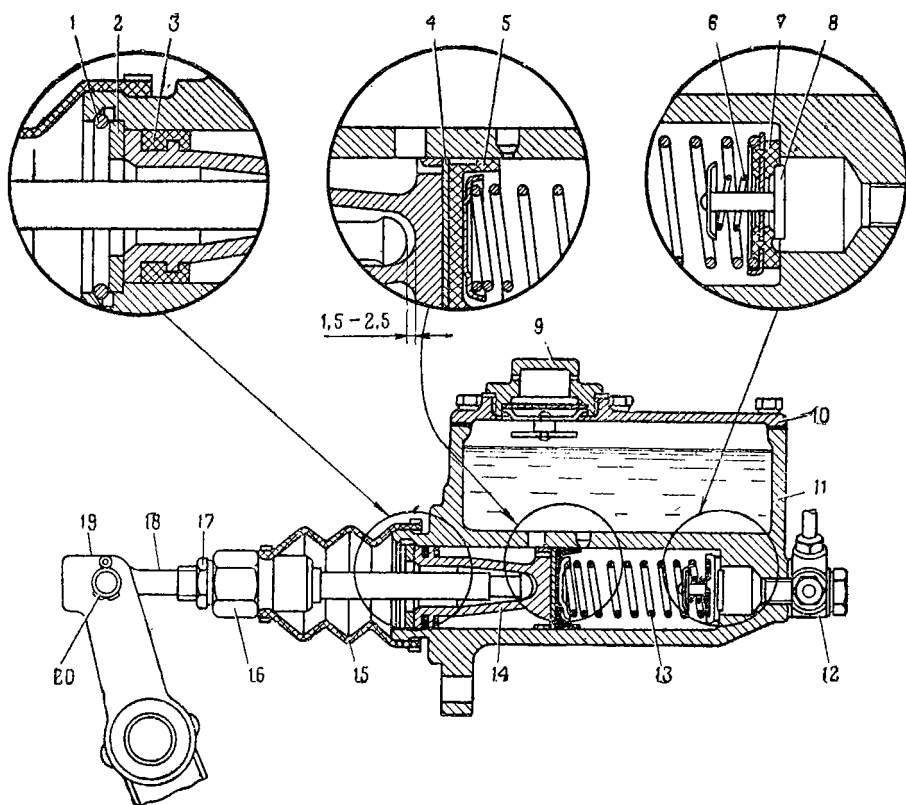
Регулировка зазора между толкателем и поршнем главного цилиндра: 1 — пружинное кольцо; 2 — упорная шайба; 3 — уплотнительное кольцо; 4 — звездообразная плоская пружина; 5 — манжета; 6 — пружина перепускного клапана; 7 — обратный клапан; 8 — перепускной клапан; 9 — пробка; 10 — крышка; 11 — корпус; 12 — штуцер; 13 — пружина обратного клапана; 14 — поршень; 15 — защитный кожух; 16 — толкатель; 17 — контргайка; 18 — тяга; 19 — педаль; 20 — палец
